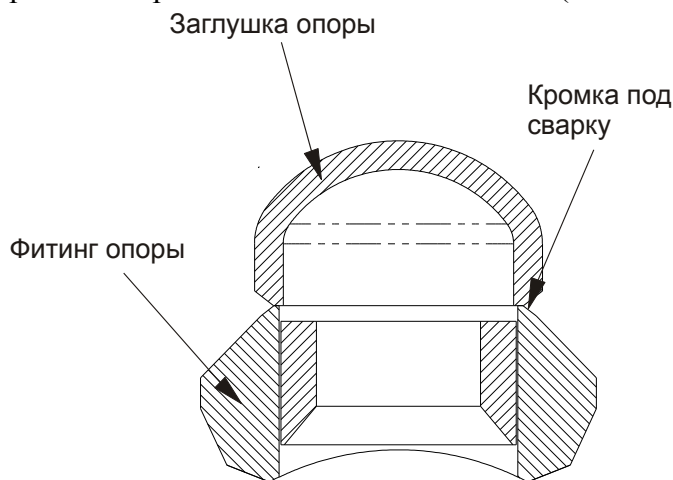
“Сварная” опора с противоположной стороны
